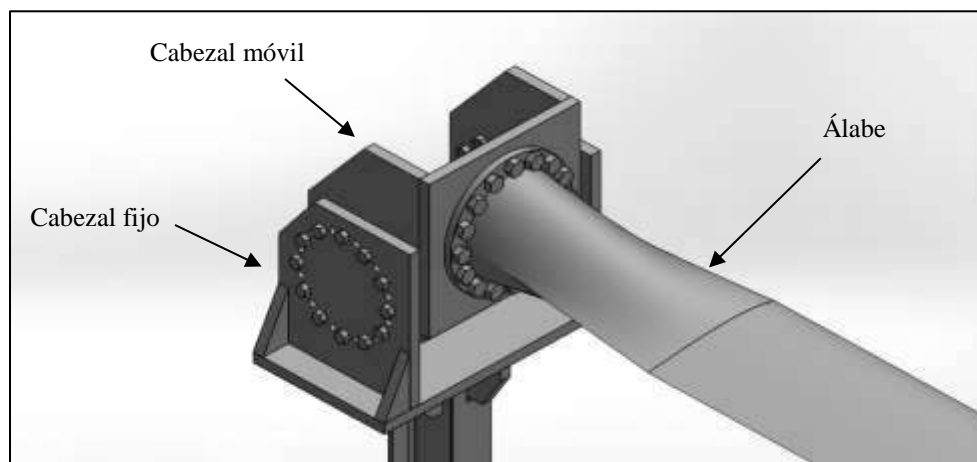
Cabezal 1 del banco de pruebas. Fuente: SOLIDWORKS 2017.
